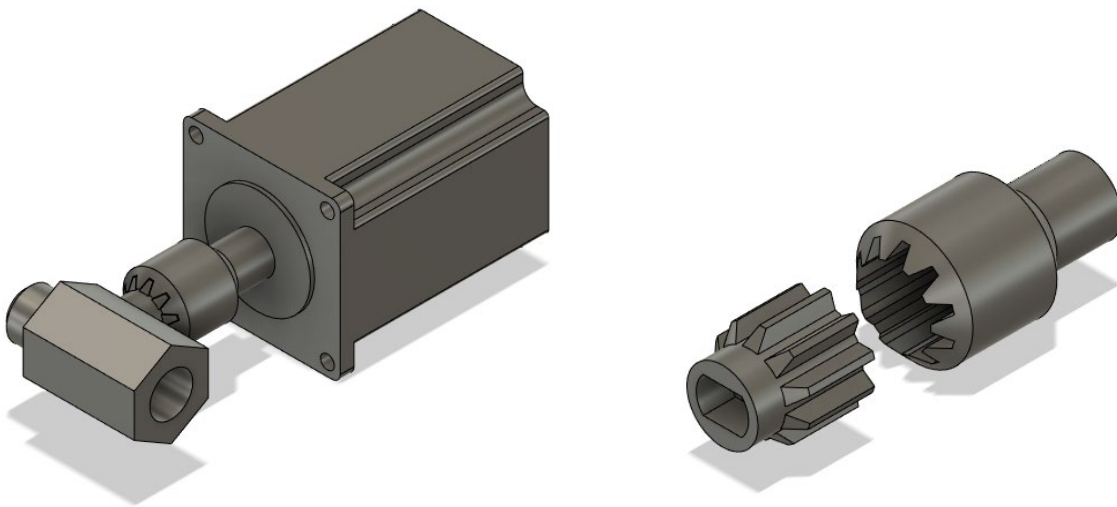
CAD-File des 3D-Druck-Adapters zur Verbindung von Kugelventil und Schrittmotor
